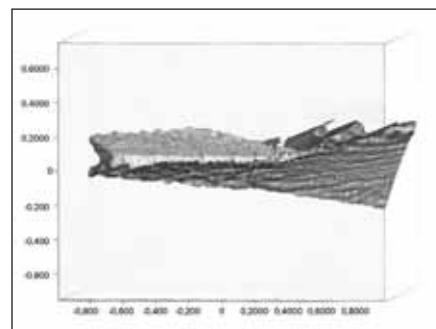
Режущая кромка метчика после его изготовления, заусенец на режущей кромке. Рисунок: OTEC GmbH, ФРГ
